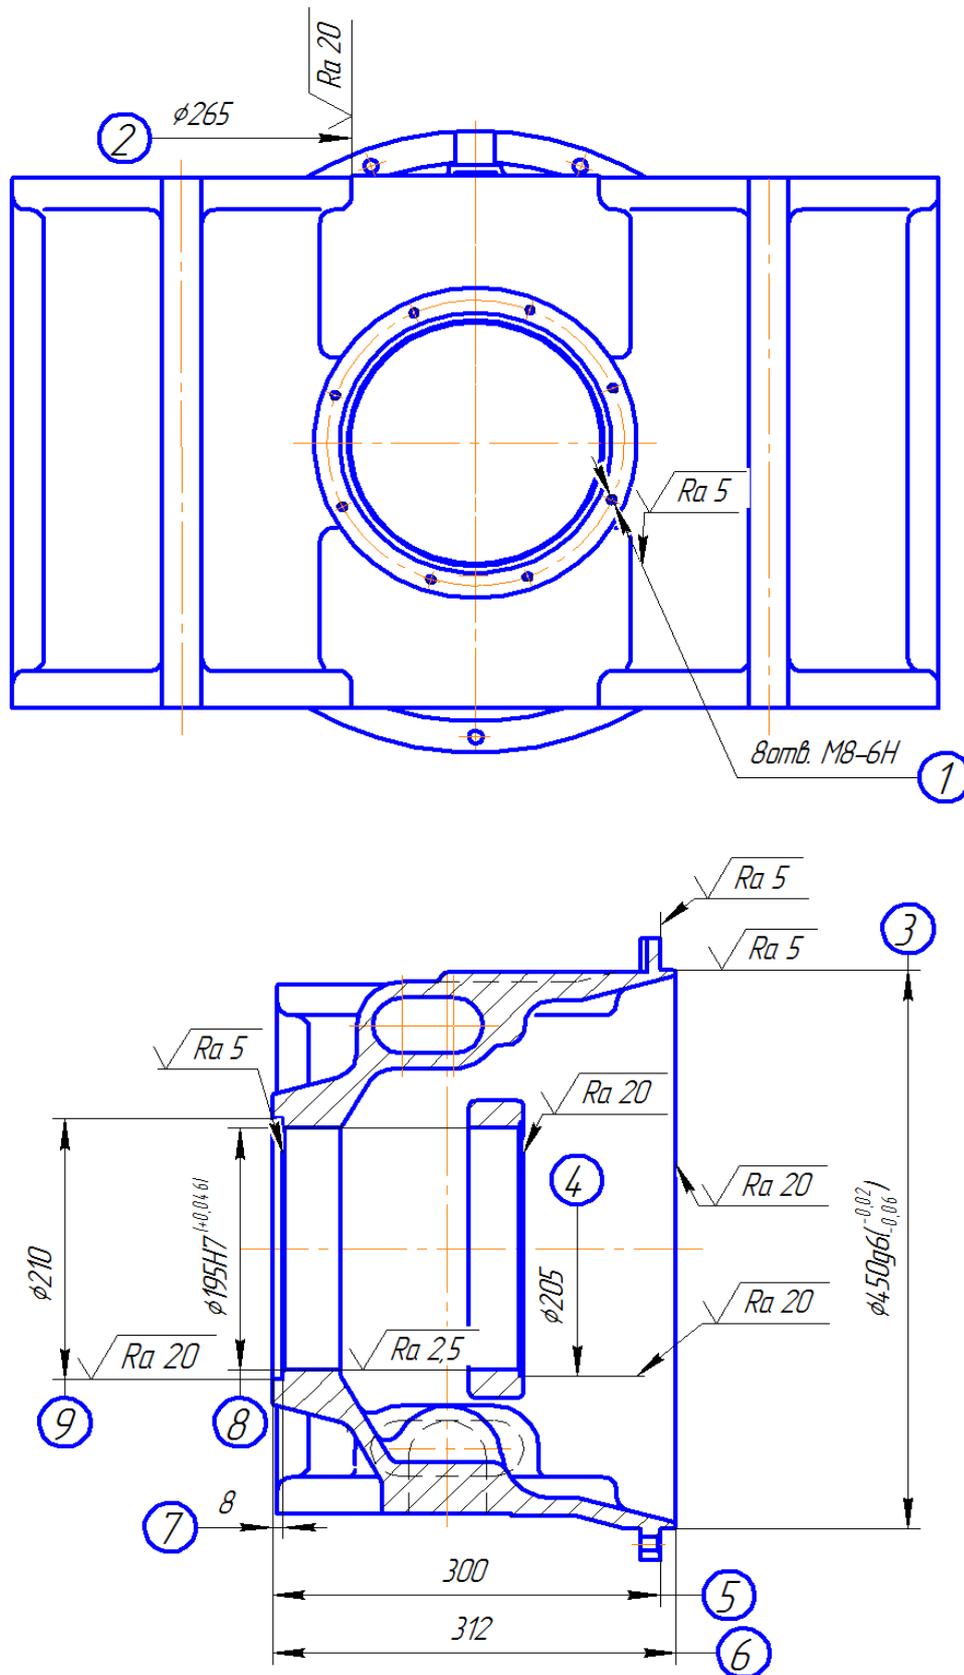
Эскиз детали «Корпус привода вентилятора» (сечение А-А)
